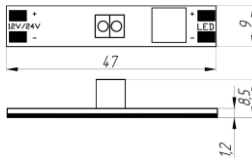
Габаритные размеры и Сенсорный выключатель GL-12V60WIRS.
